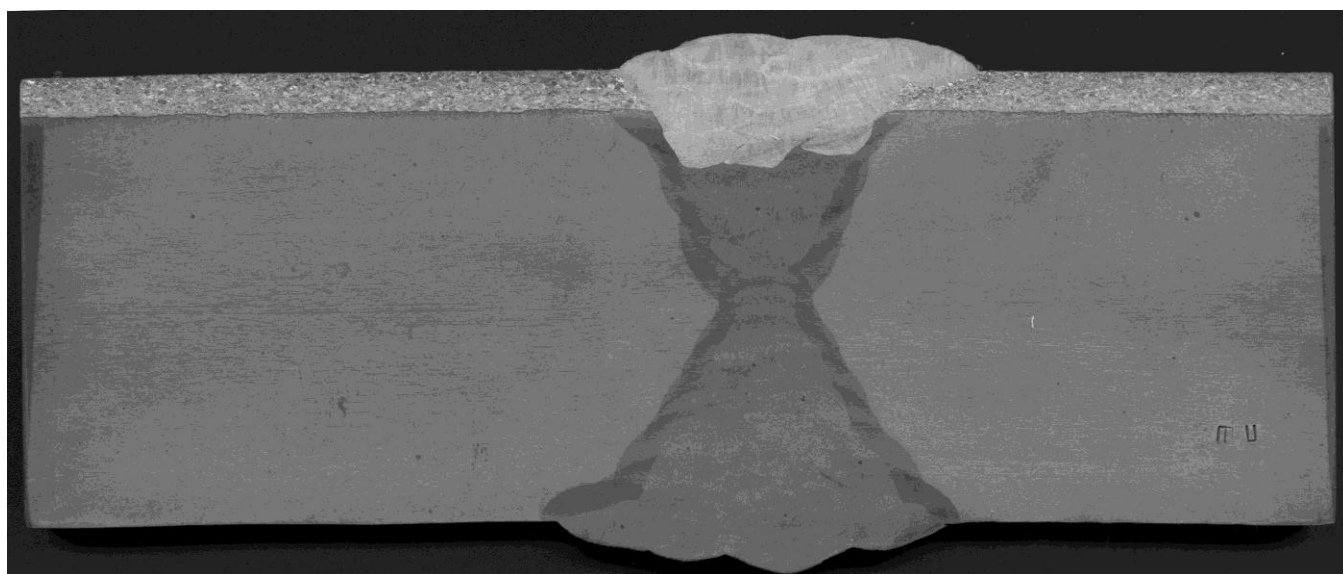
Макроструктура сварного соединения плакированной стали.
